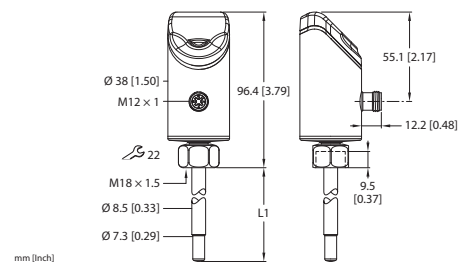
Abmessungen – Sensor ohne Einschraubadapter
